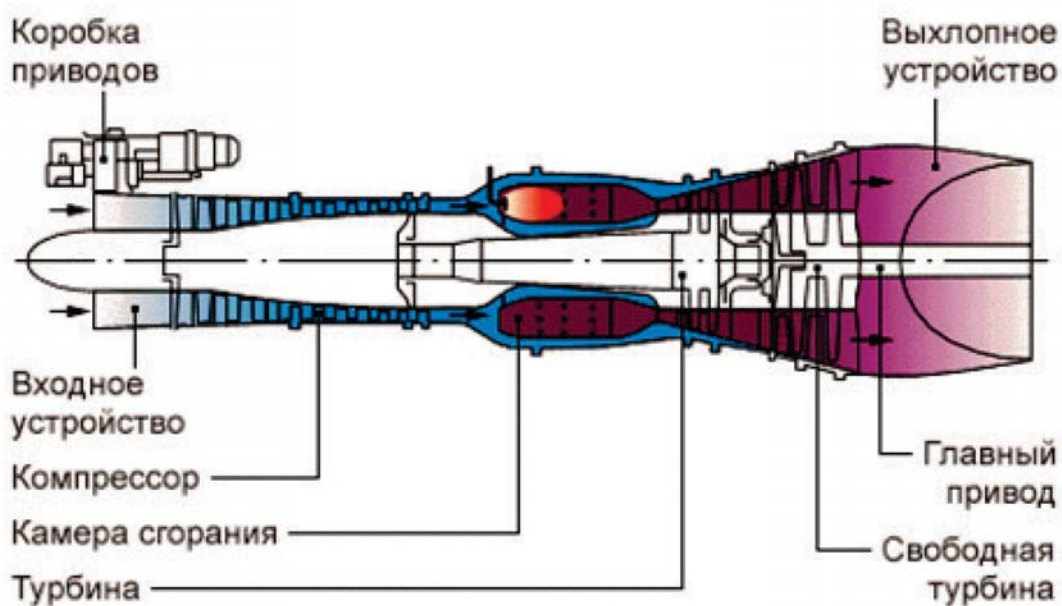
Конструкция двигателя ТВ2-117А (АГ)
